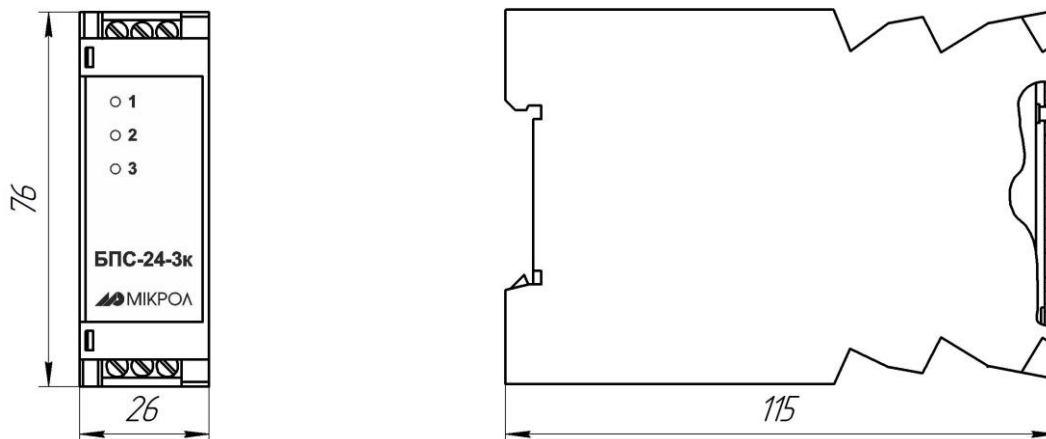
Внешний вид и габаритные размеры БПС-24-3к-Н15
